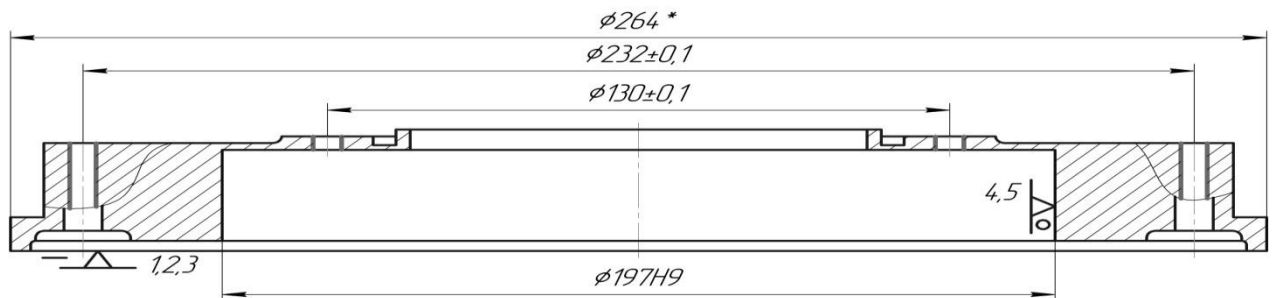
Схема базування заготовки на жорсткій оправці
